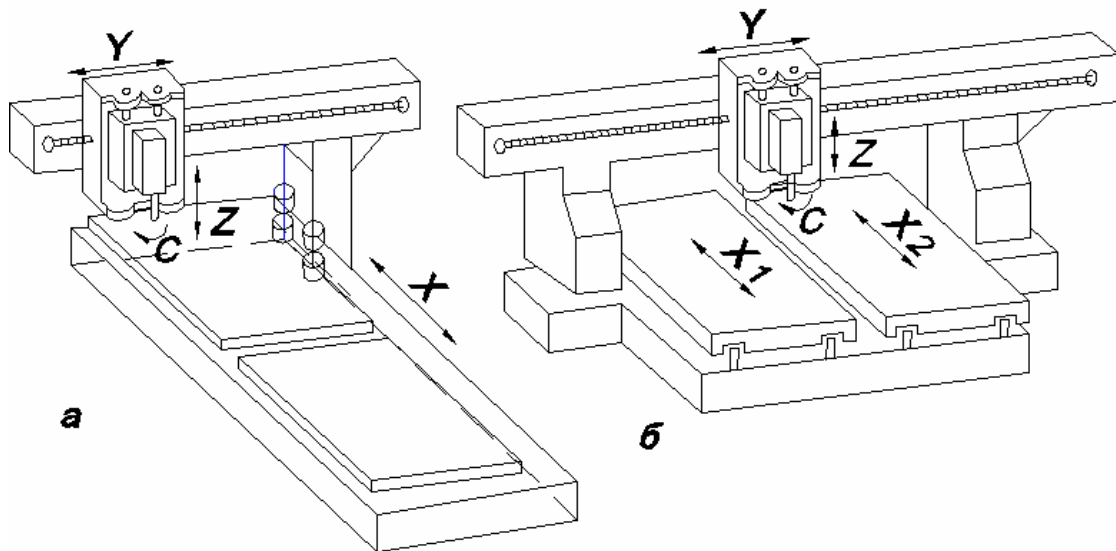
Координатные компоновки обрабатывающих центров: а – консольного типа; б – портального типа
